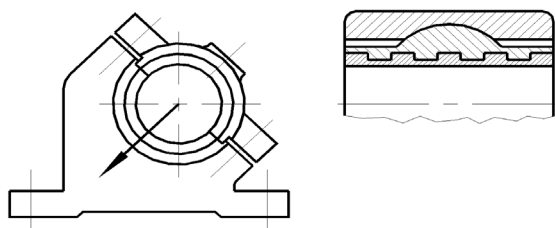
Разъемный самоустанавливающийся подшипник
